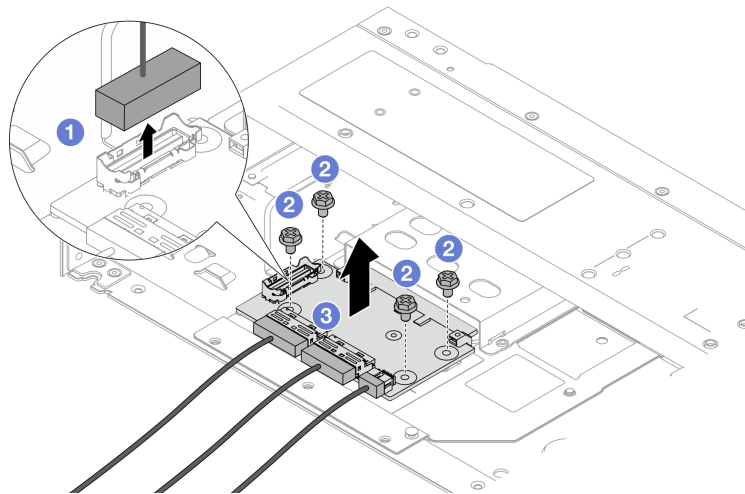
Extracción de la tarjeta de interposición de OCP frontal
